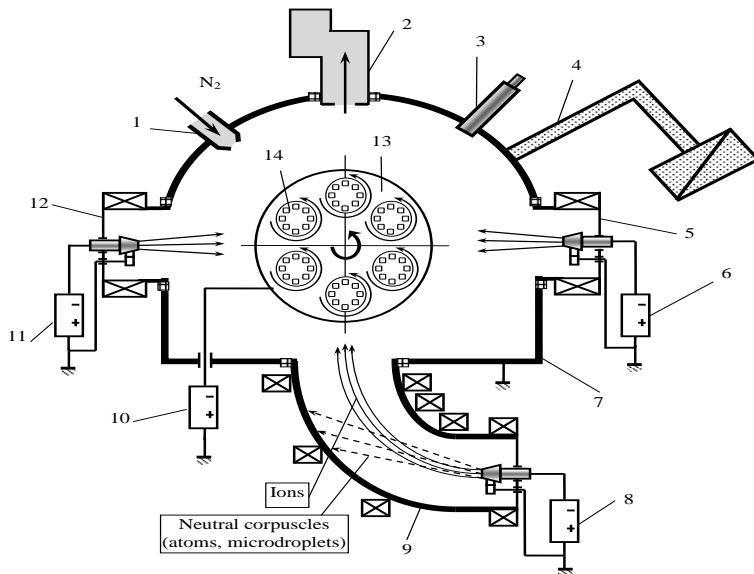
Схема плазменно-дуговой установки ВИТ-2 для нанесения покрытий на режущий инструмент:
